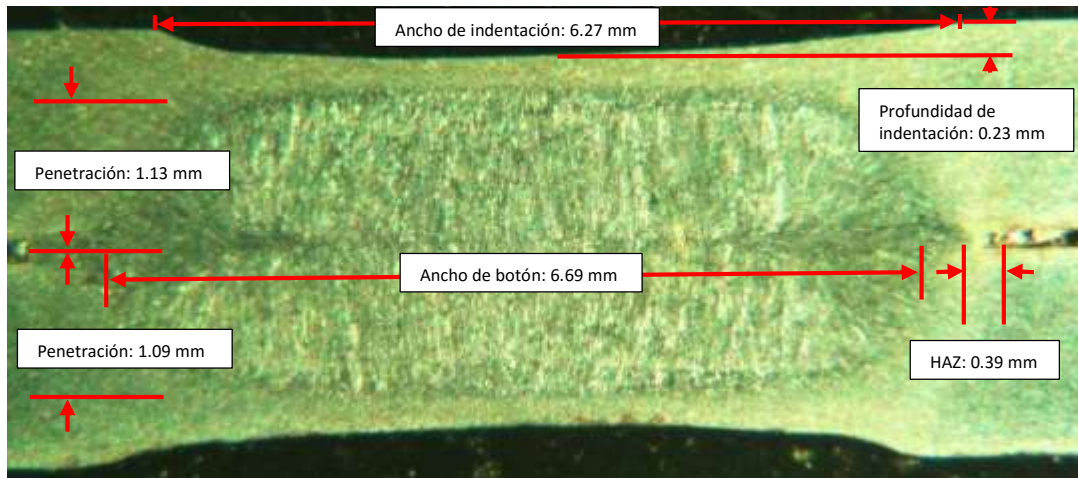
Mediciones realizadas en el botón de soldadura número 11.
